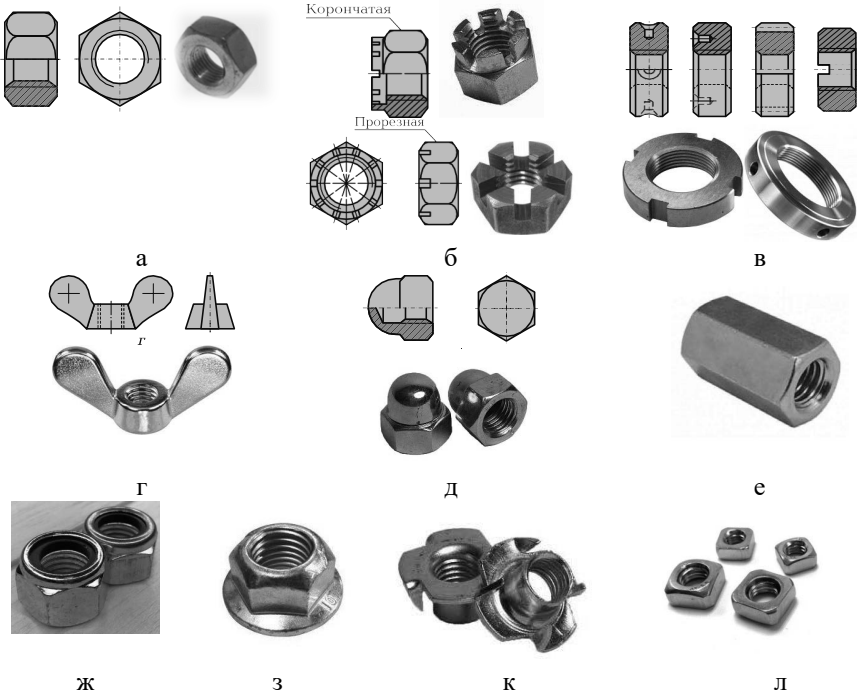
Гайки: а – шестигранна; б – шестигранні корончаста і прорізна; в – круглі; г – гайка-баранчик; д – ковпачкова; е – стяжна; ж – гайка з нейловою вставкою; з – гайка з фланцем; к – врізна; л – квадратні
